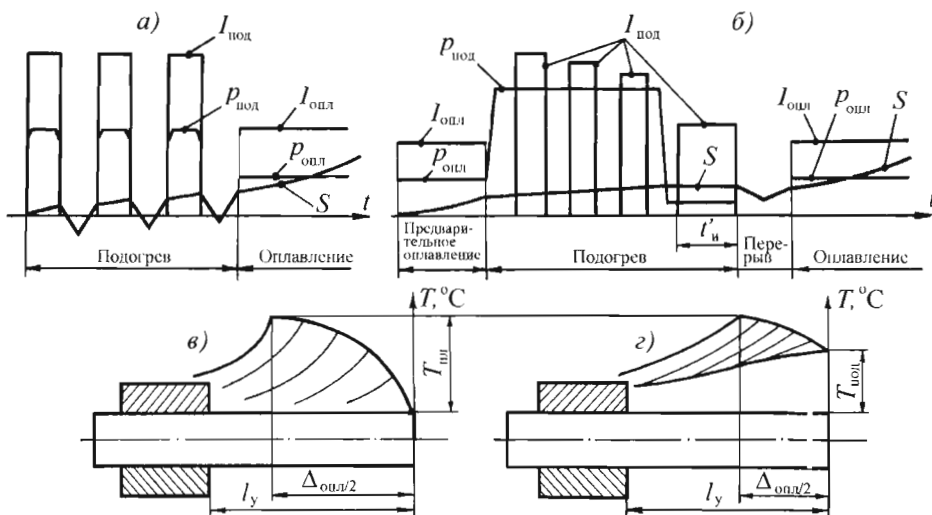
Способы подогрева деталей перед стыковой сваркой непрерывным оплавлением:
